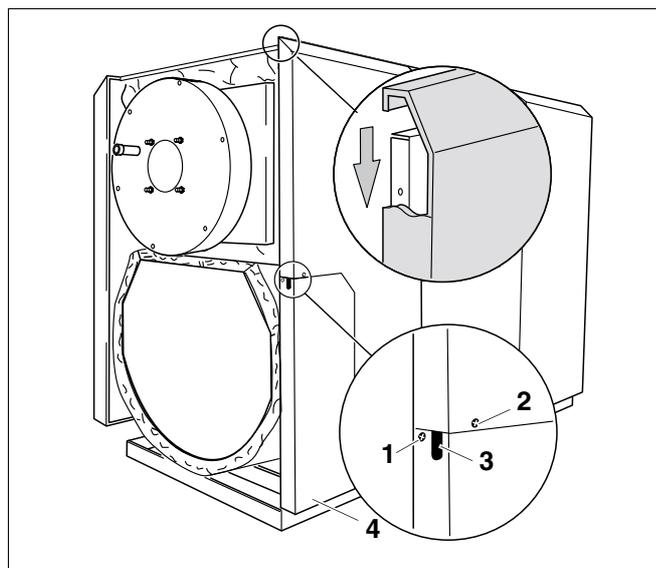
Montaggio dei pannelli laterali nella parte superiore
